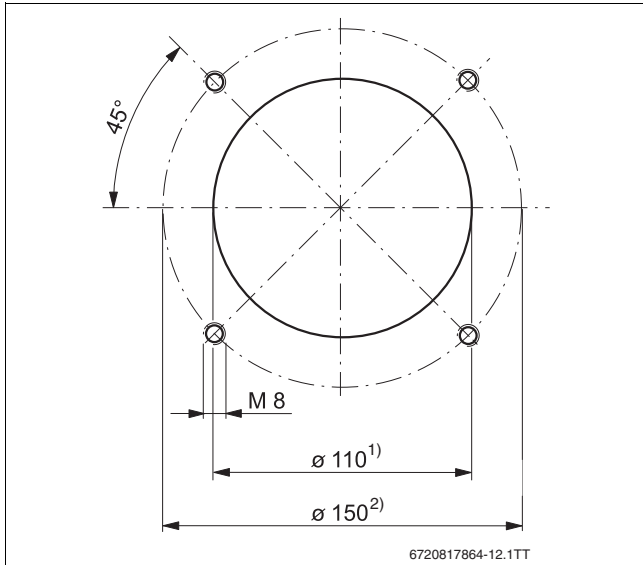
Circuito de orificio de la puerta del quemador (brida de conexión según DIN EN 226, dimensiones en mm)
